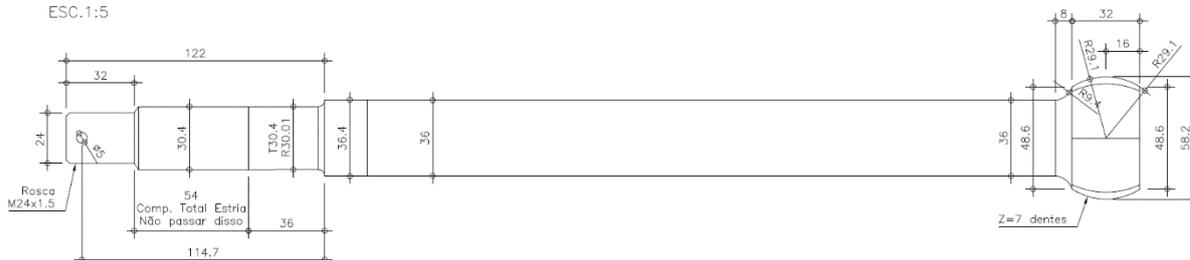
desenho técnico da ponta de eixo “BF Câmbios”
